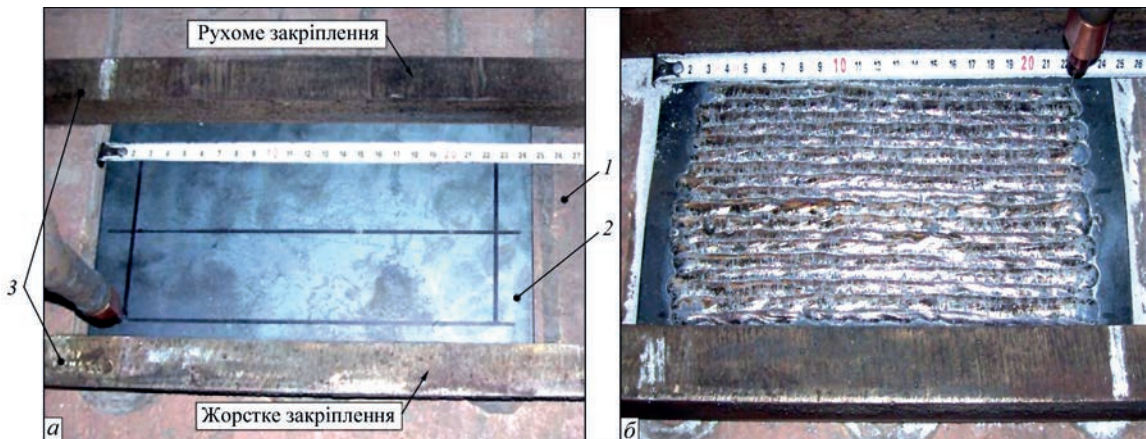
Спосіб закріплення пластин на зварювальному столі (*a*): 1 – зварювальний стіл з мідною пластиною, 2 – пластина, що наплавляється, 3 – притисні планки; (*б*) – зовнішній вигляд пластини після наплавлення
